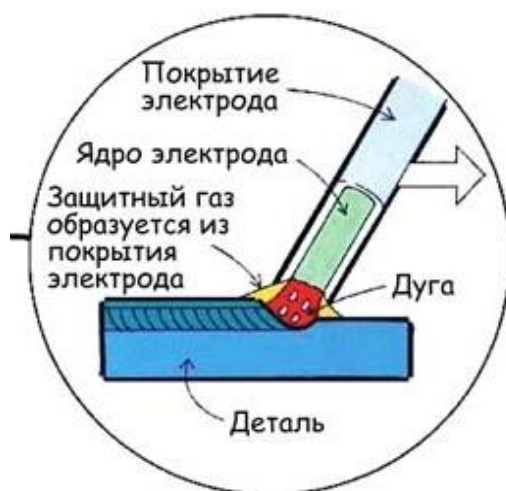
Схема выполнения ручной дуговой сварки
